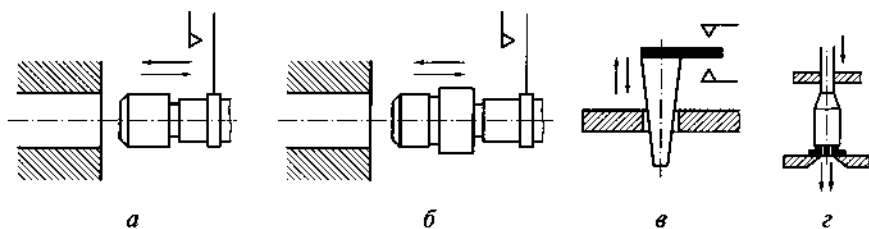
Схемы автоматического контроля (а...г) диаметров отверстий
